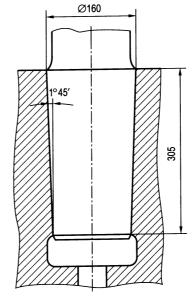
Соединение штока с бабой ковочного молота
